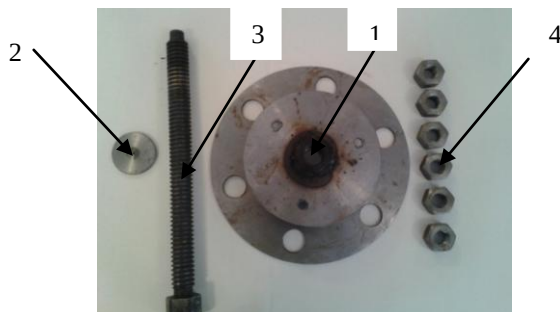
Состав приспособления для демонтажа опорного катка БМП-3
